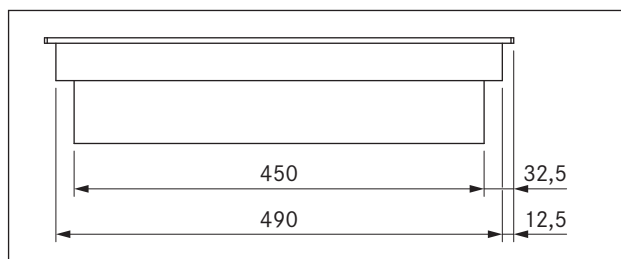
CKIW dimensioni apparecchio vista laterale
